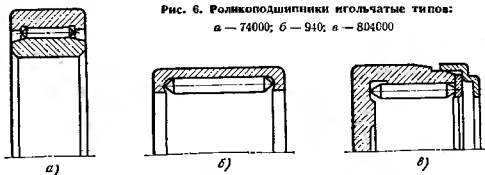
Роликоподшипники игольчатые типов: а — 74000; б — 910; в — 804000
